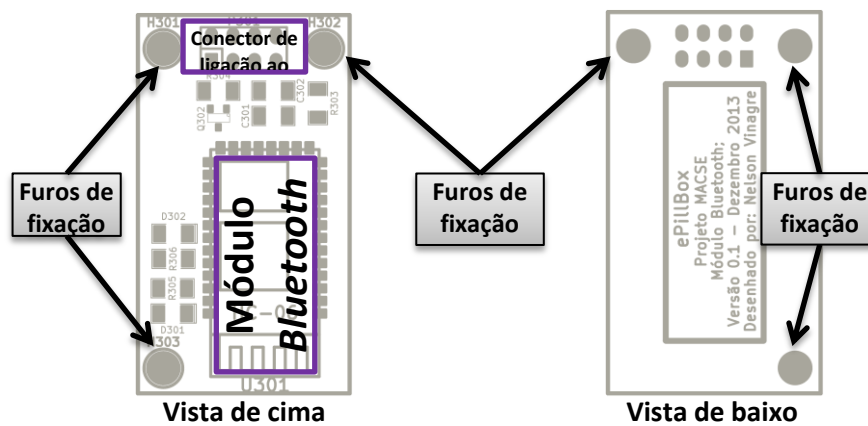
Placa de circuito impresso do Módulo de Bluetooth.
